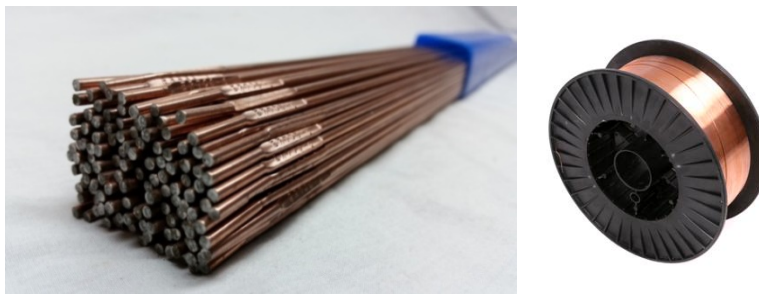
Varillas y bobinas de acero ER70-6 para soldadura.
